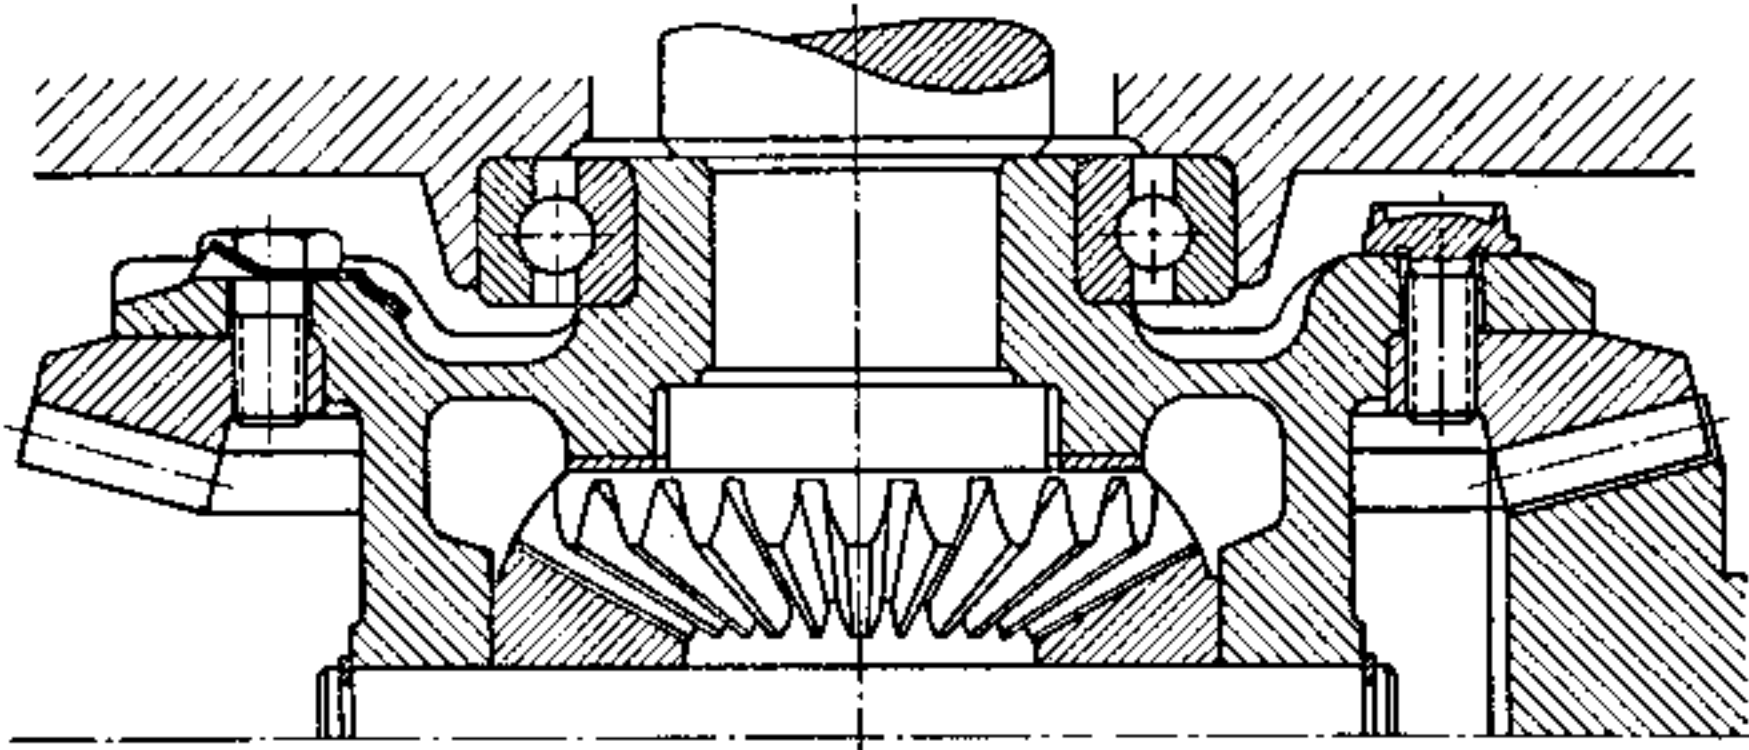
Schraubenverbindung am Tellerrad eines Ausgleichgetriebes.
